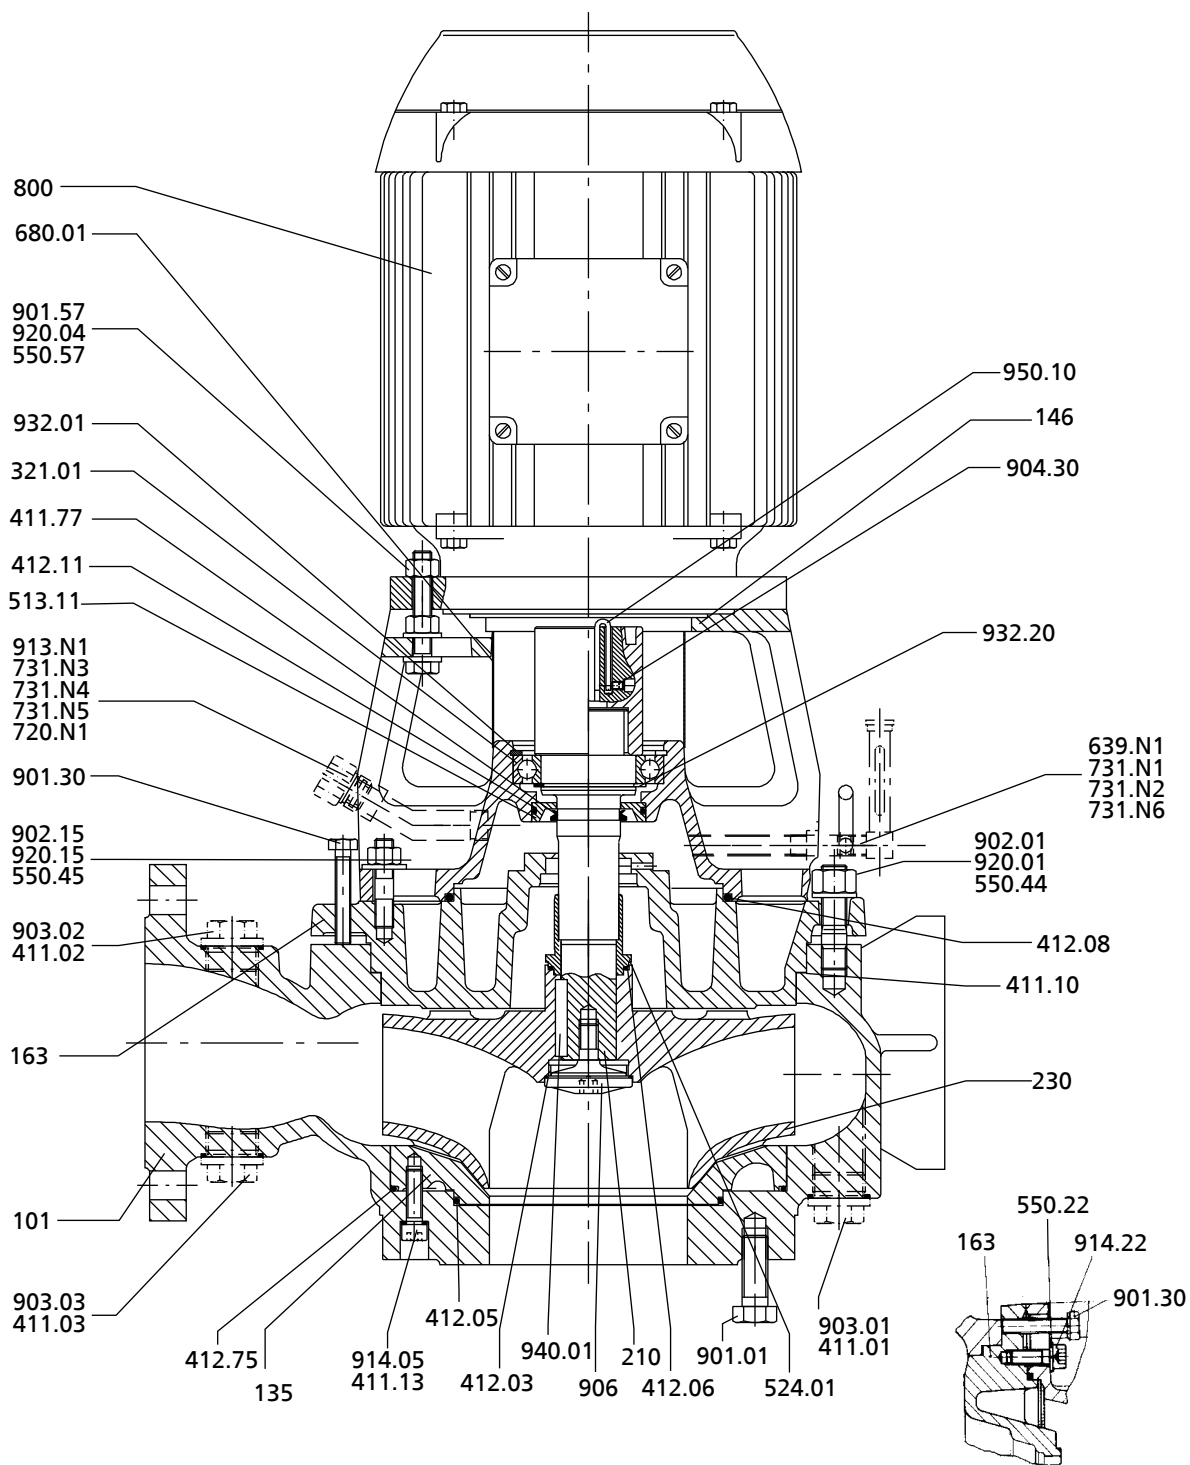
Сборочный чертеж исполнения GNG, GDNG
